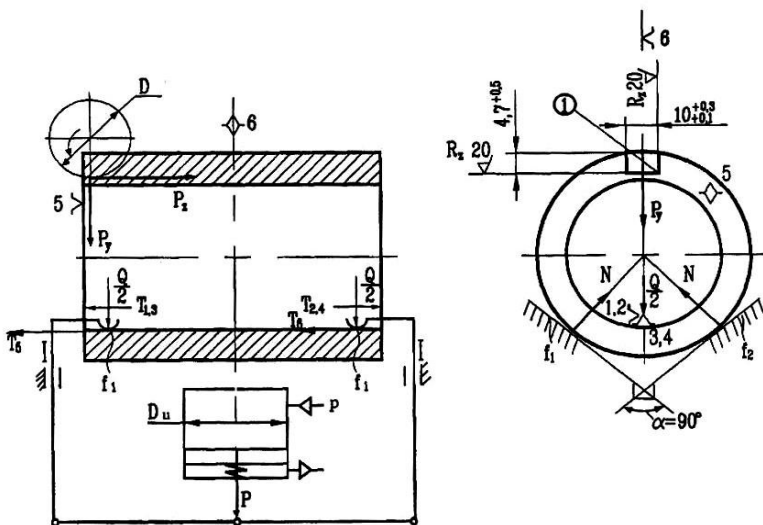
Принципиальная расчетная схема приспособлении для фрезерования паза
